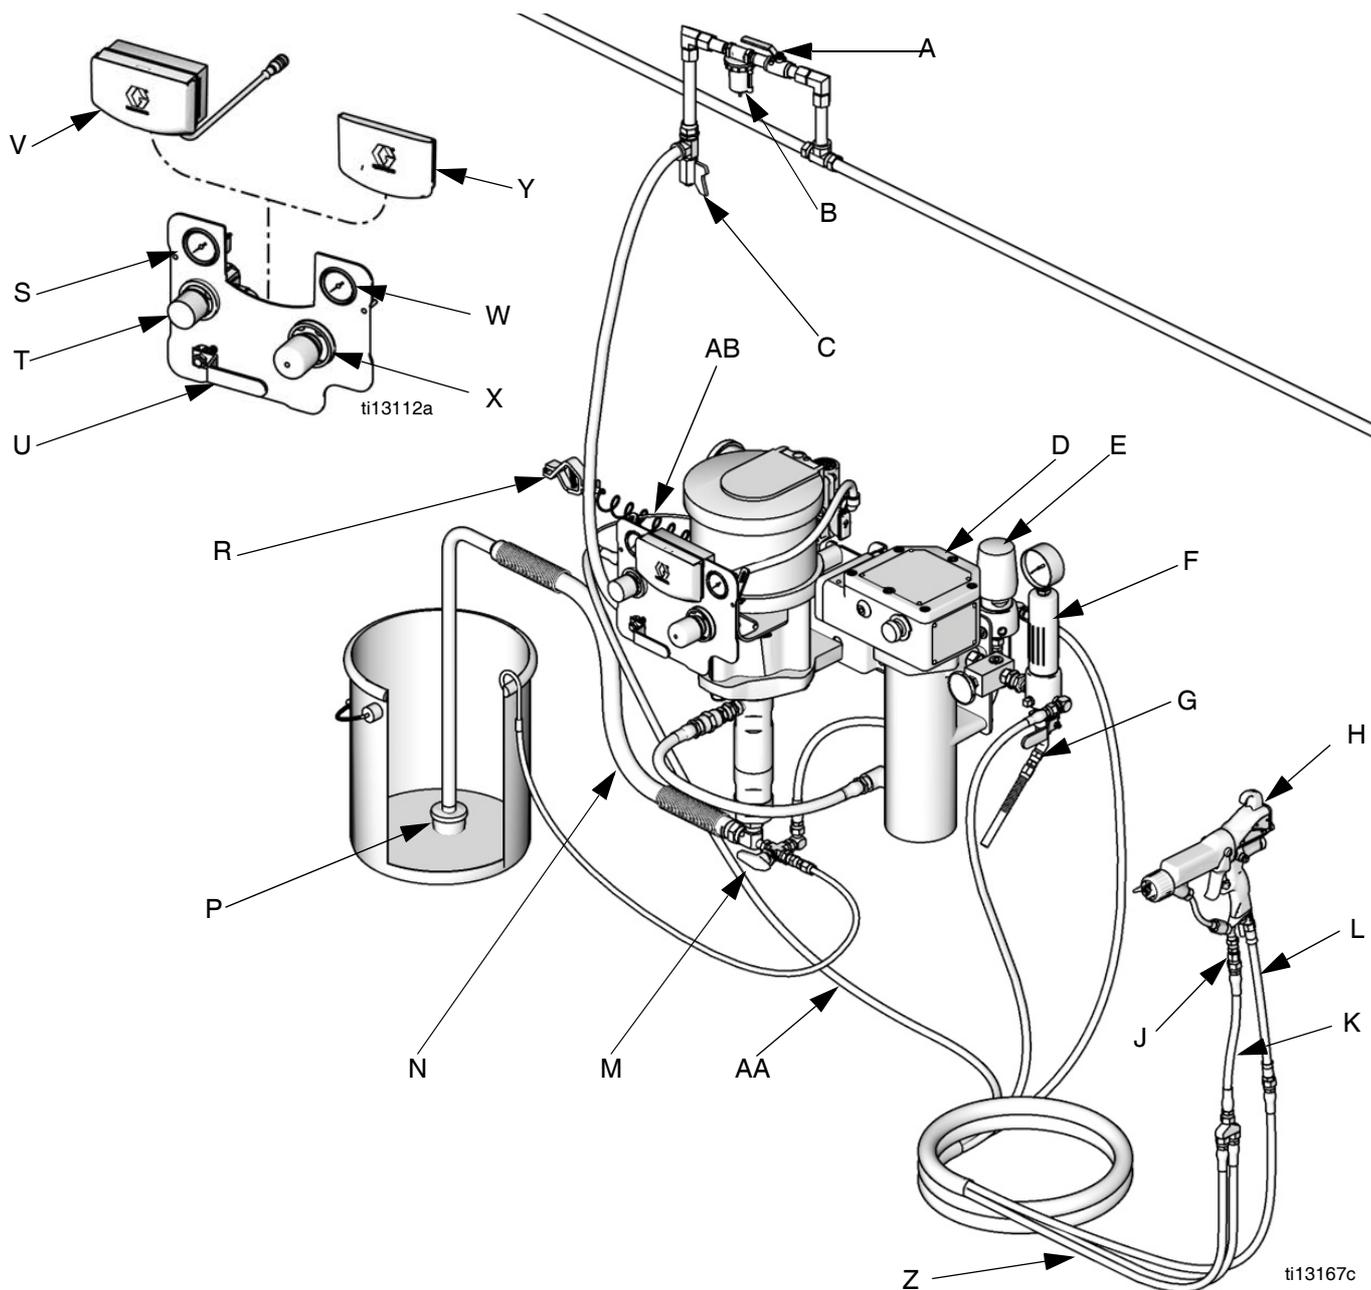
Installation type, modèle G30W86 chauffé illustré
